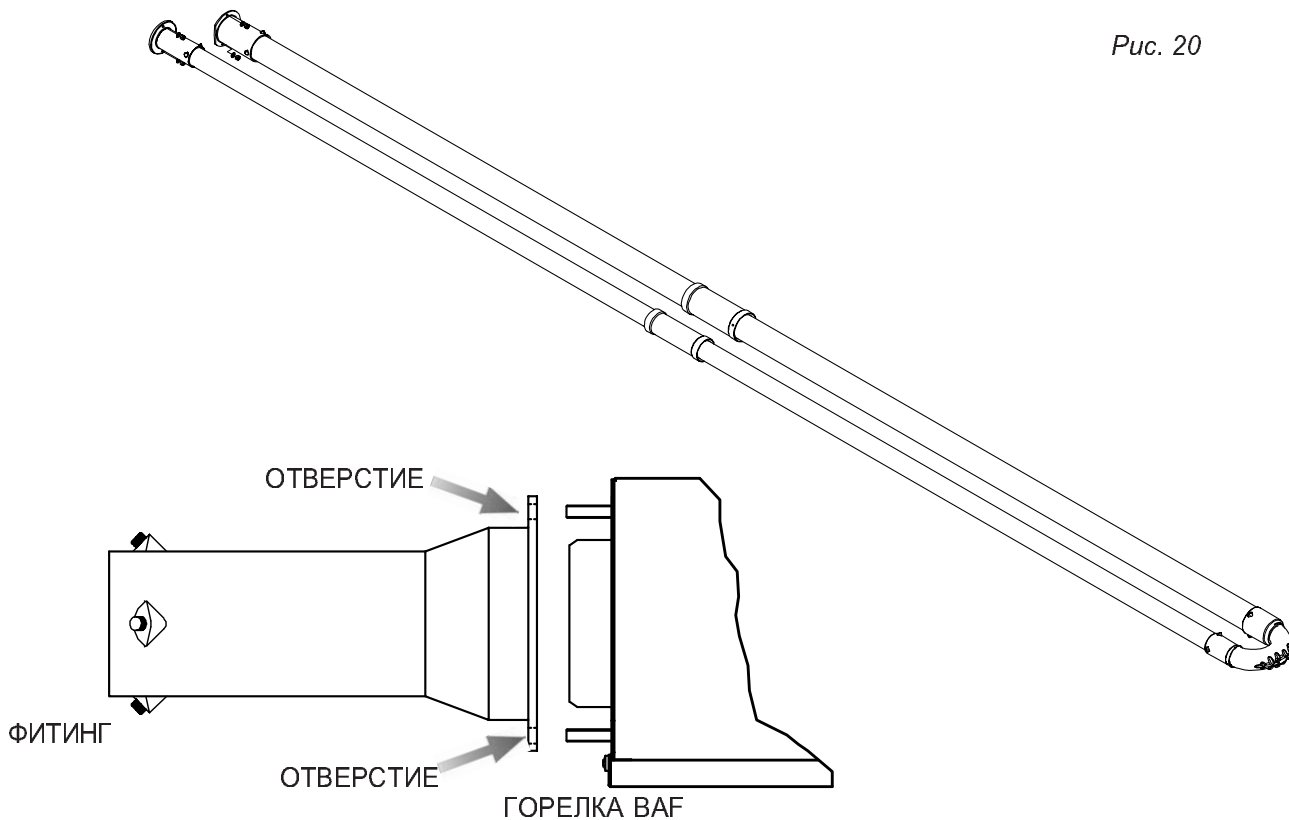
Положение отверстий для крепления вытяжного вентилятора и горелки
